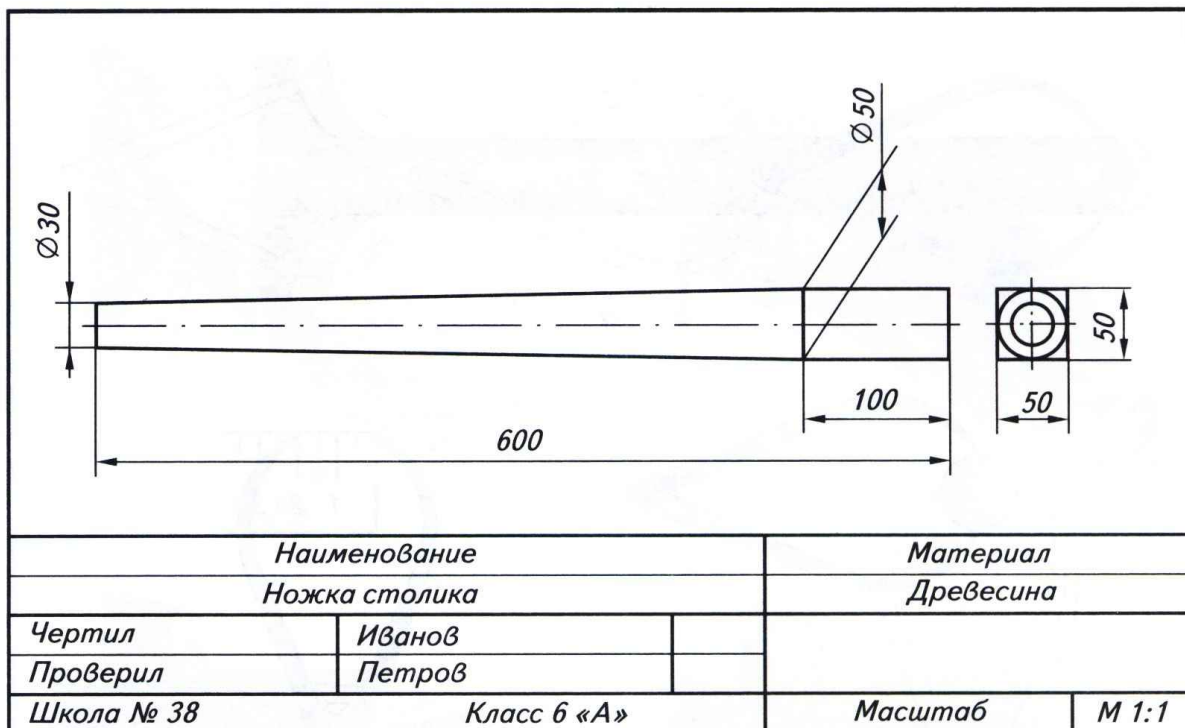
Чертёж детали «ножка столика для балкона» (см. рис. 6, д)
